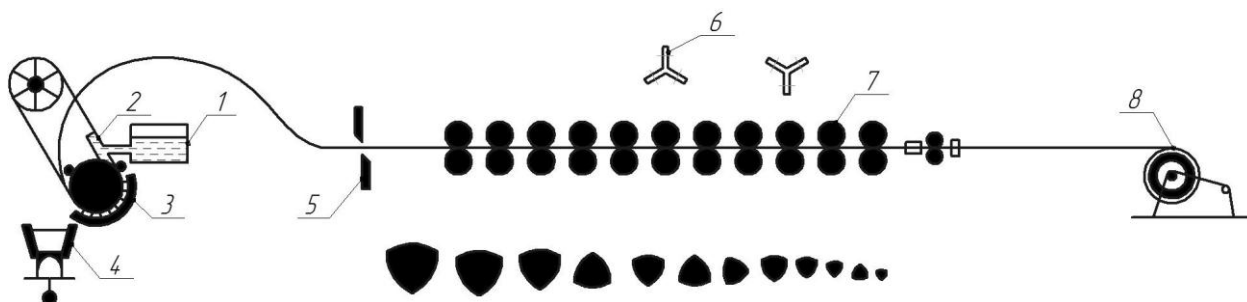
Схема ливарно-прокатного стану із кристалізатором роторного типу для алюмінієвого дроту: 1 – проміжна ванна; 2 – дозатор; 3 – кристалізатор; 4 – поперечний переріз кристалізатора; 5 – летучі ножиці (аварійні); 6 – схема розташування валків у двох суміжних клітках; 7 – тривалковий безперервний стан; 8 – моталка
